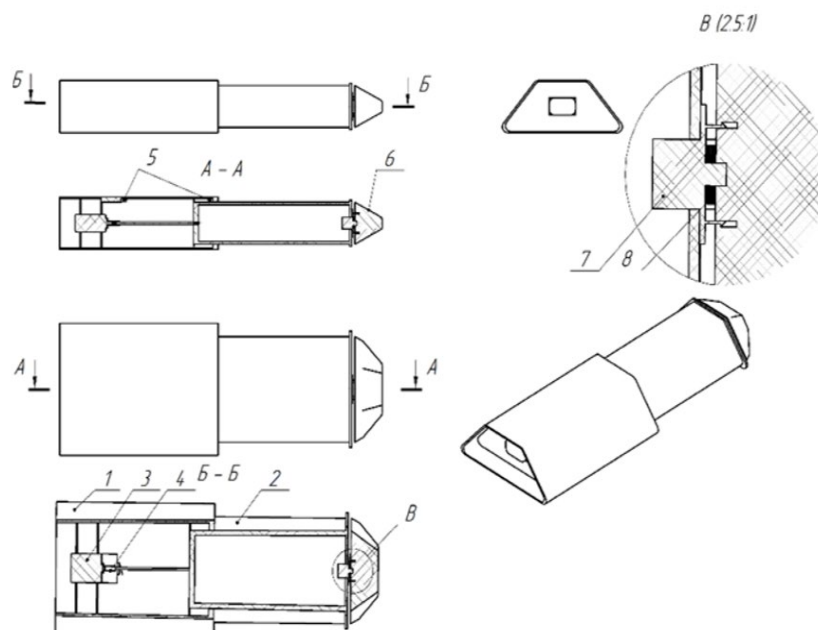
Эскиз разрабатываемой посадочной опоры: 1 — корпус; 2 — шток; 3 — электродвигатель; 4 — соединительная муфта; 5 — концевой выключатель; 6 — кнопка концевой выключателя; 7 — концевой выключатель (внешний); 8 — пружина
